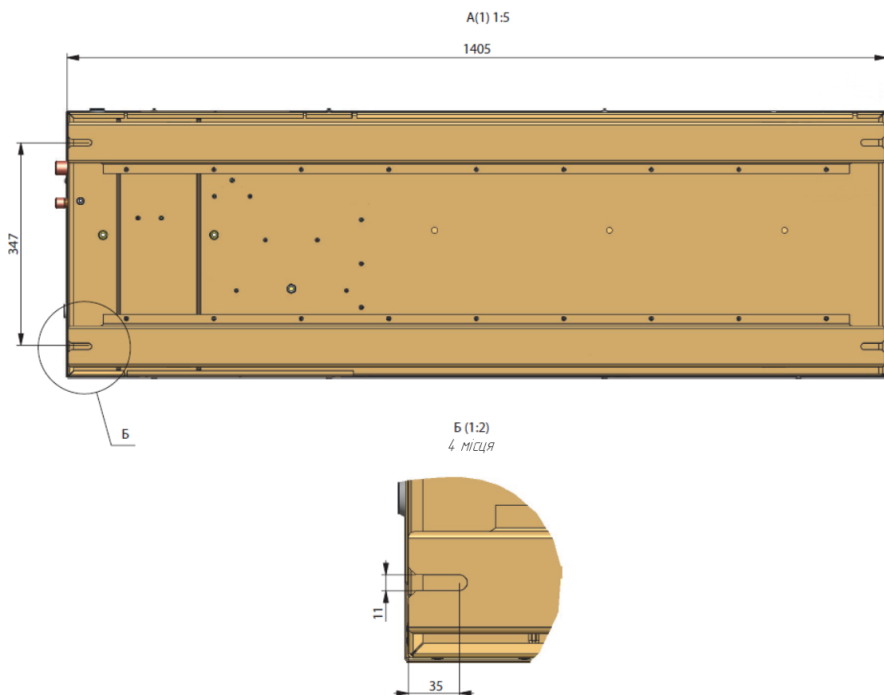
Загальний вид агрегату типу МАКК-110-201
